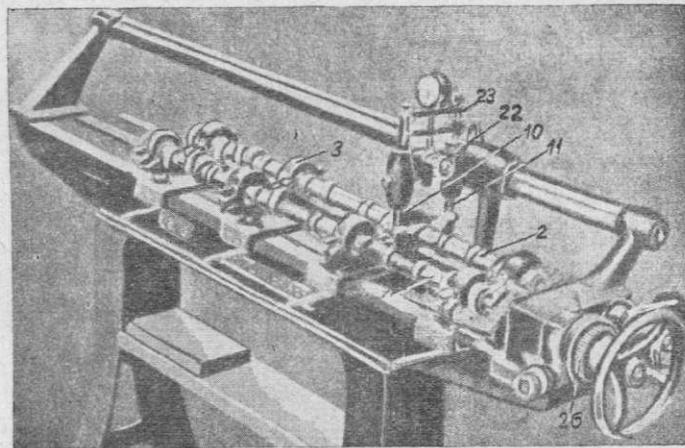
Станок фирмы Фриц Вернер для проверки профиля кулачков распределительного вала.
